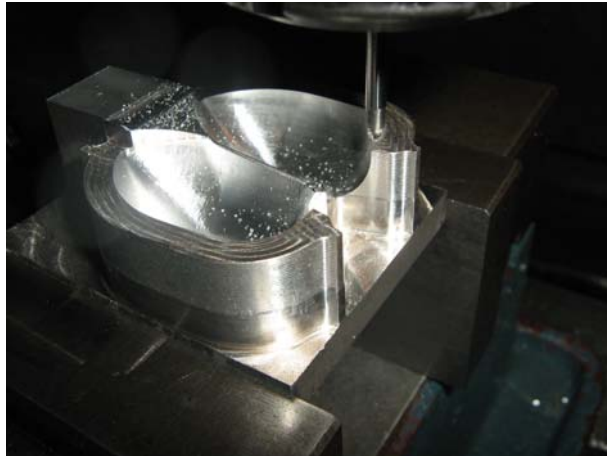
Maquinado álabe Pelton en Fresadora C.N.C
